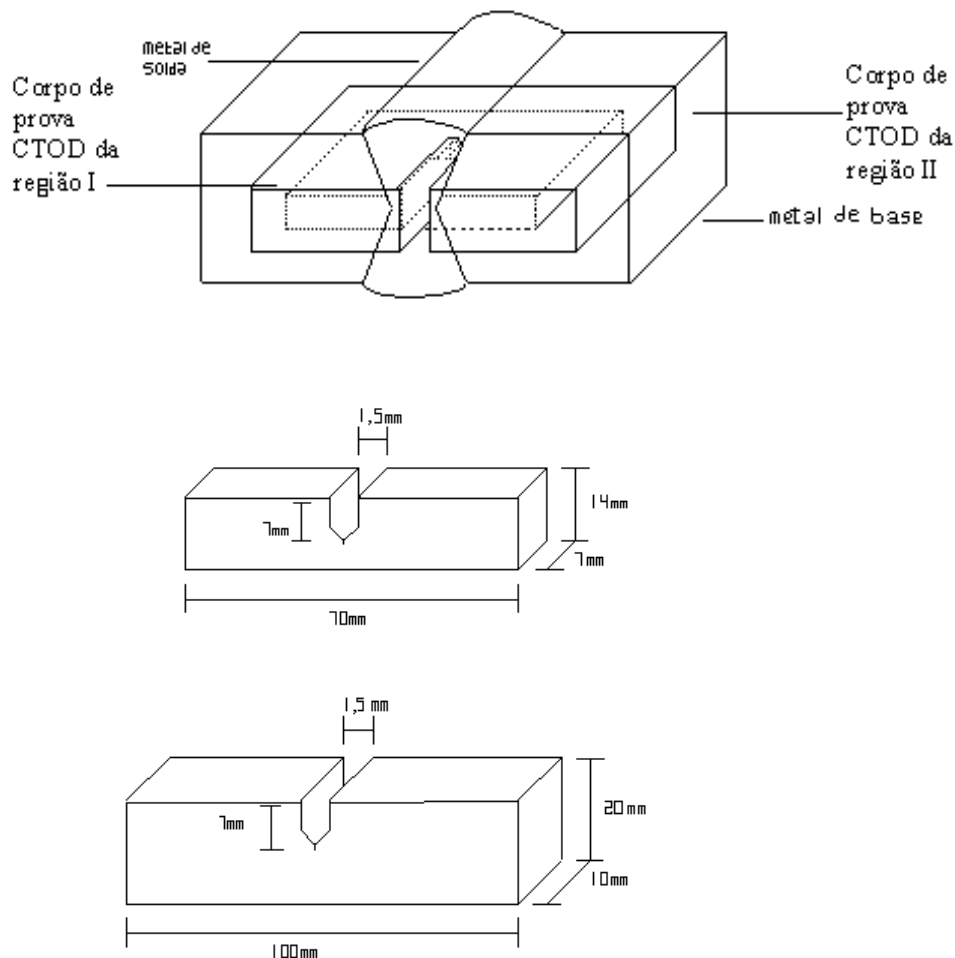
Ilustração esquemática do posicionamento de usinagem dos corpos de prova CTOD no metal de solda.
